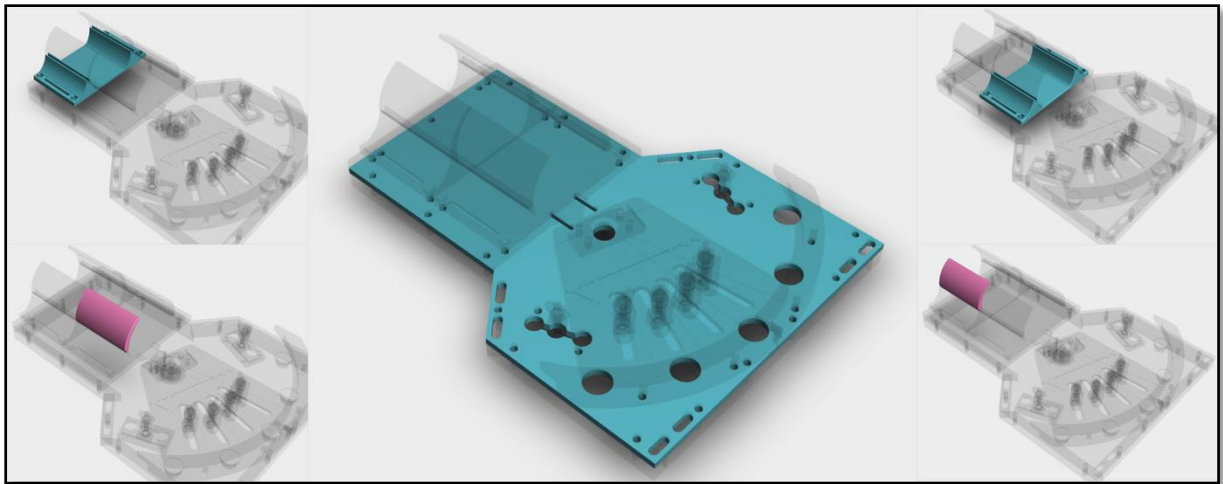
Vues 3D de la partie fixe ou support du dispositif GWMD.
